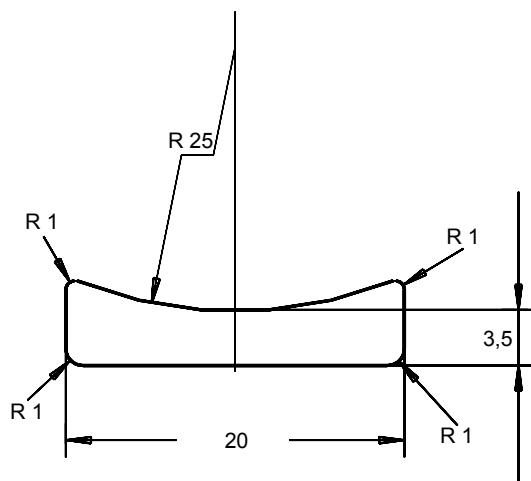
Dimensions de la buse d'extrusion de la pâte
